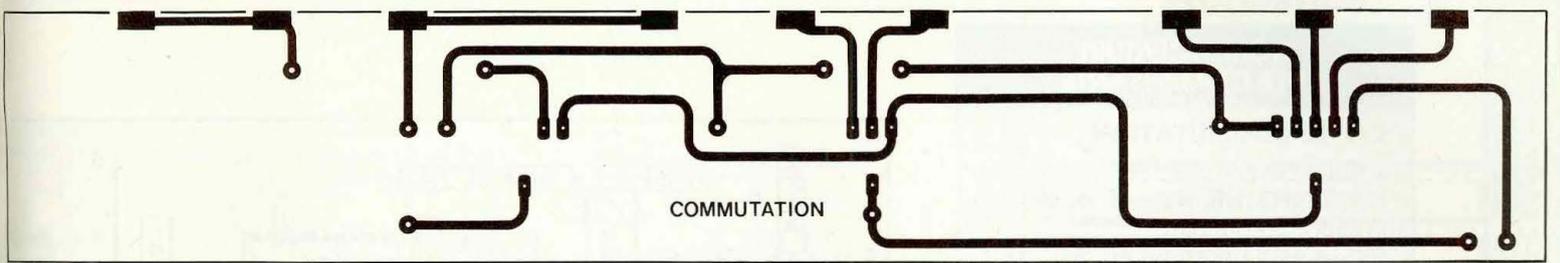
Assemblage face arrière. Superposition des deux cartes de commutation.
